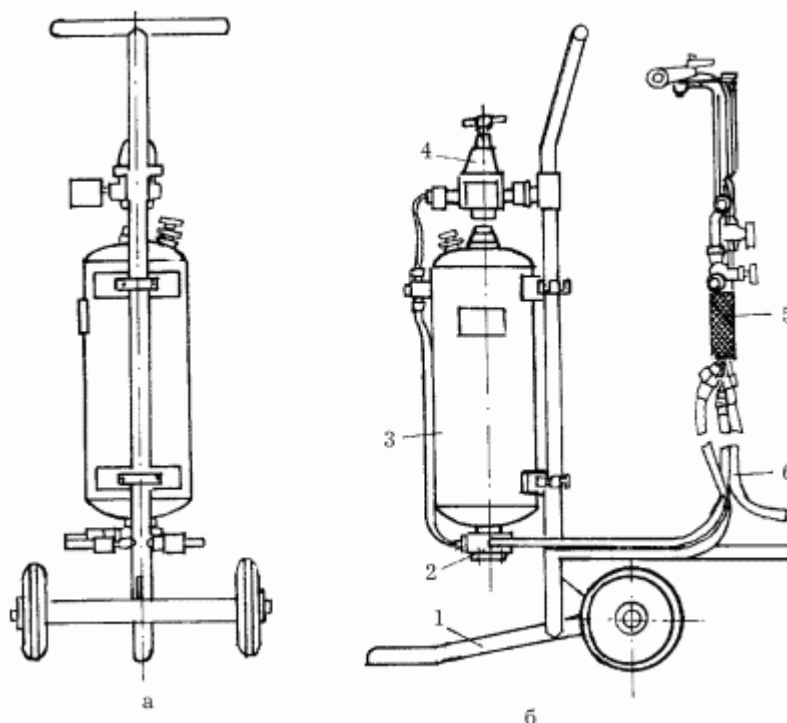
Установка кислородно-флюсовой резки: а – вид спереди; б – вид сбоку; 1 – тележка, 2 – циклон, 3 – флюсопитатель, 4 – редуктор кислорода, 5 – резак, 6 – шланги.
